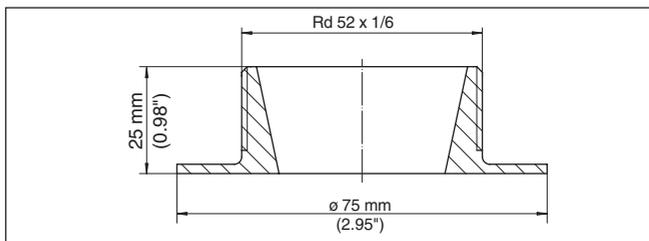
Medidas racor para soldar conexión cónica DN 25
